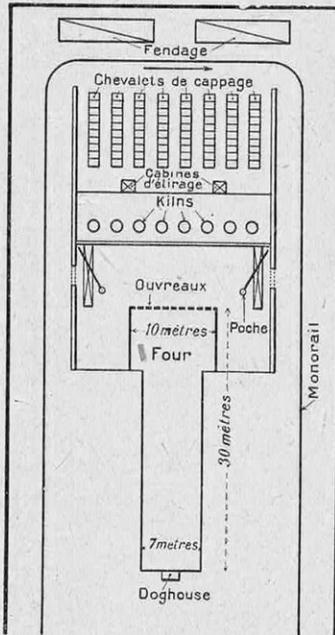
PLAN GÉNÉRAL DE LA VERRERIE A VITRES DE CHALON-SUR-SAONE (AMERICAN WINDOW GLASS)
